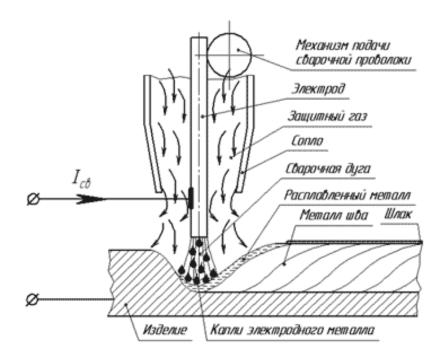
Схема сварки в защитных газах
